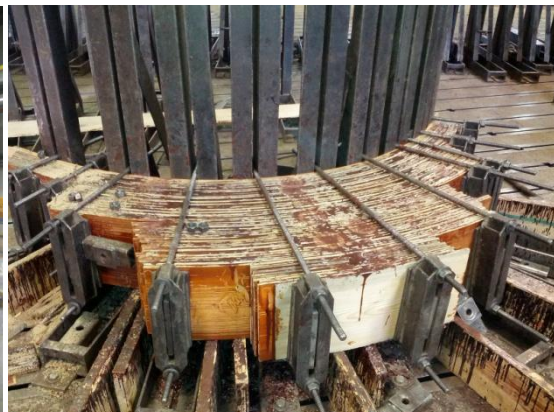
Detalle de postes y de guías en una prensa horizontal para laminación de una viga curva.
